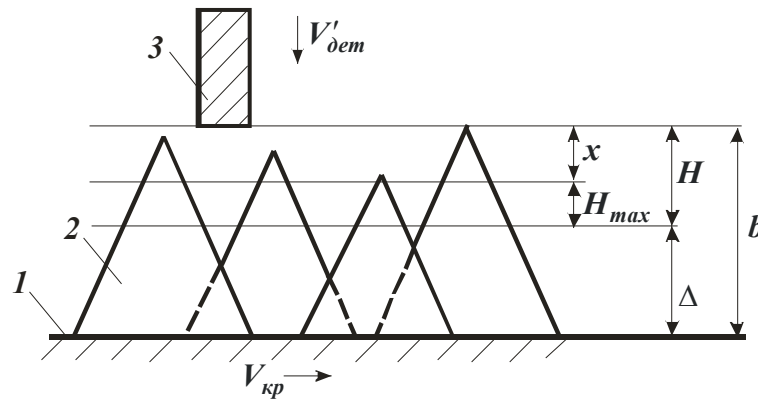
Расчетная схема параметров шлифования: 1 – связка круга; 2 – зерно; 3 – обрабатываемый образец.
